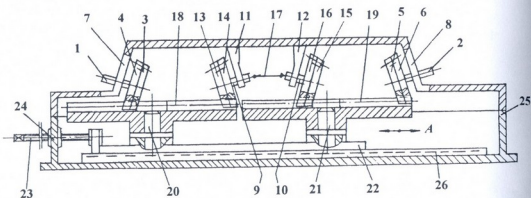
Четырехступенчатый вариатор с коническими зубчатыми колесами
